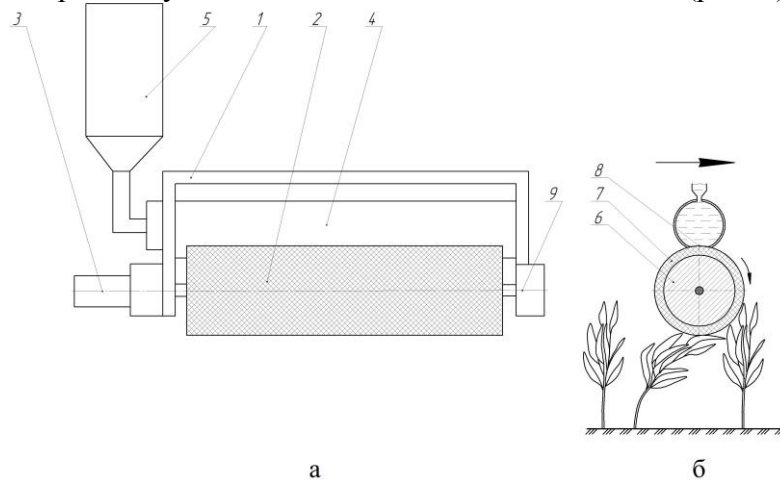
Схема пристрою для контактеного нанесення хімікатів на рослини (а) та схема роботи (б): 1 – рама; 2 – контактний валик; 3 – привод; 4 – живильний резервуар; 5 – місткість для хімікатів; 6 – пористий шар; 7 – сітка; 8 – дозуюча щілина; 9 – регулювальний механізм
